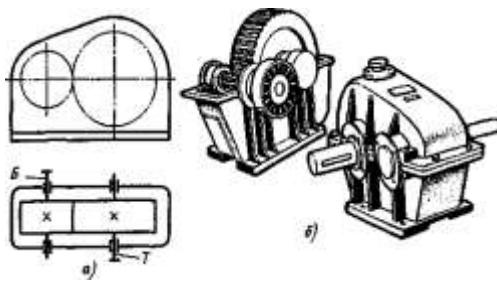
Одноступенчатый горизонтальный редуктор с цилиндрическими зубчатыми колесами:
